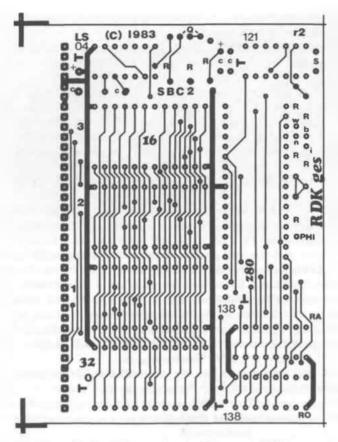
Die Bestückungsseite der Baugruppe SBC 2
